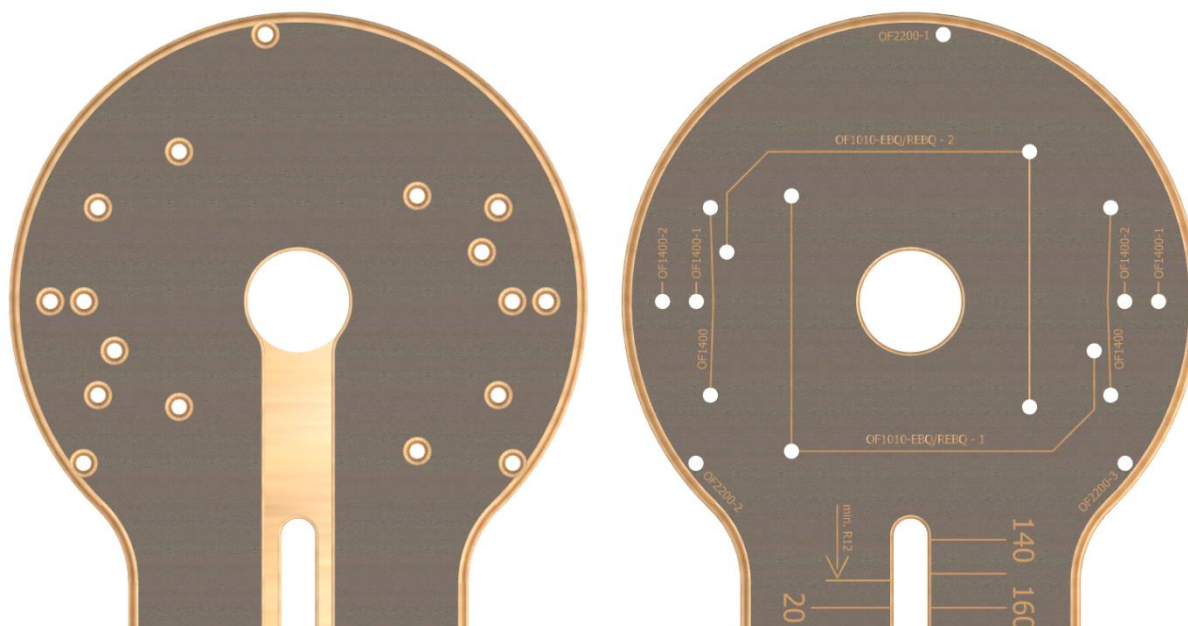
Fori di montaggio adatti al Festool OF2200 (seguono immagini)
